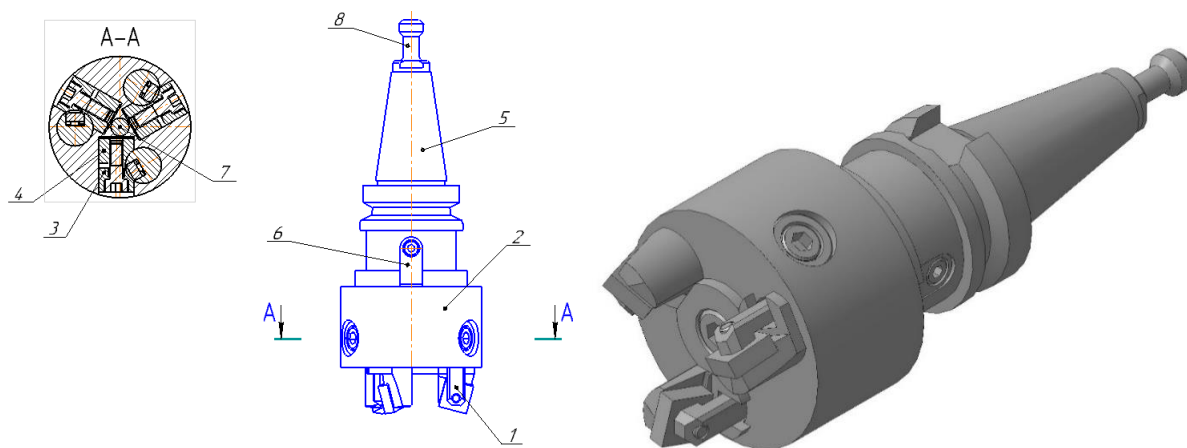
Конструктивная схема и 3D модель торцевой фрезы
